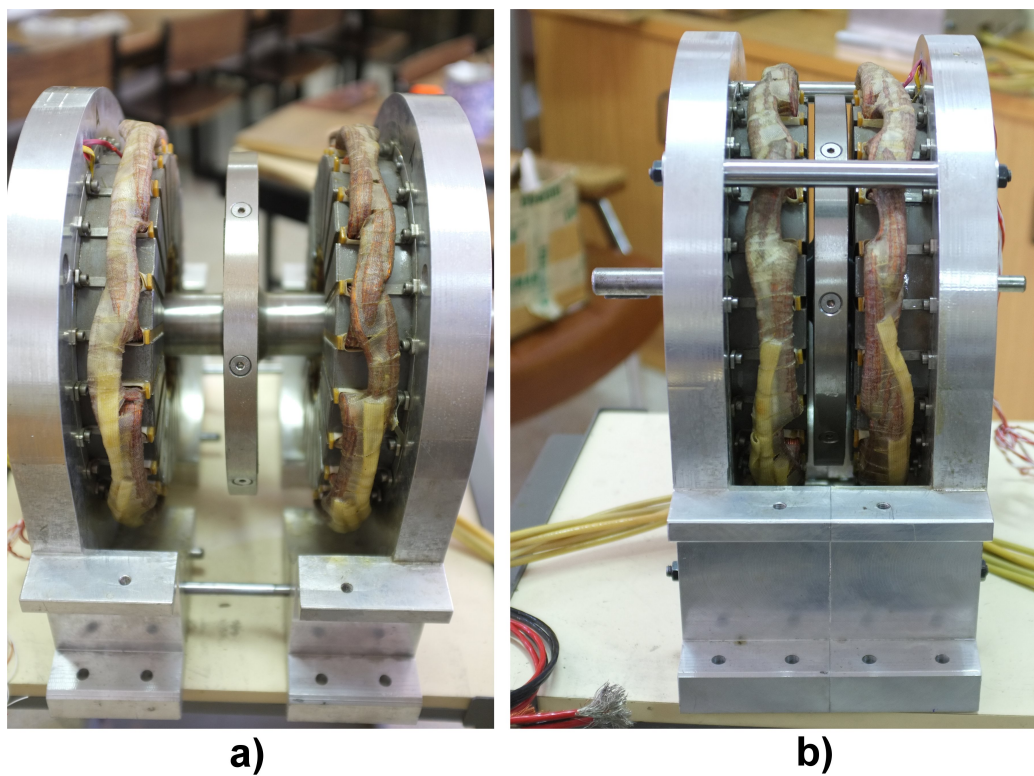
Conjunto de la máquina: a) Inicio del proceso de montaje. b) Montaje finalizado
